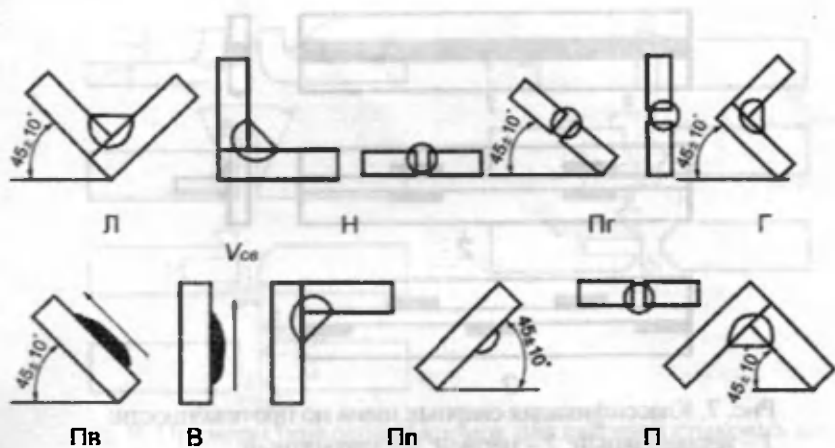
Основные пространственные положения сварки и их обозначения
